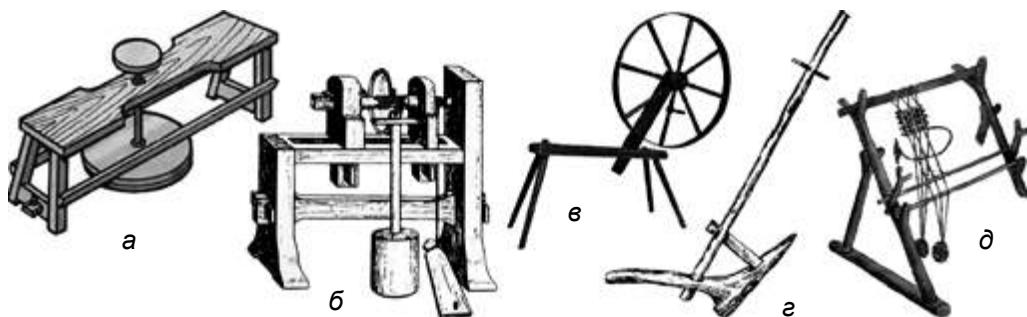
Ручные орудия труда: а – гончарный круг; б – токарный станок; в – прядка; г – рало; д – ткацкий станок
